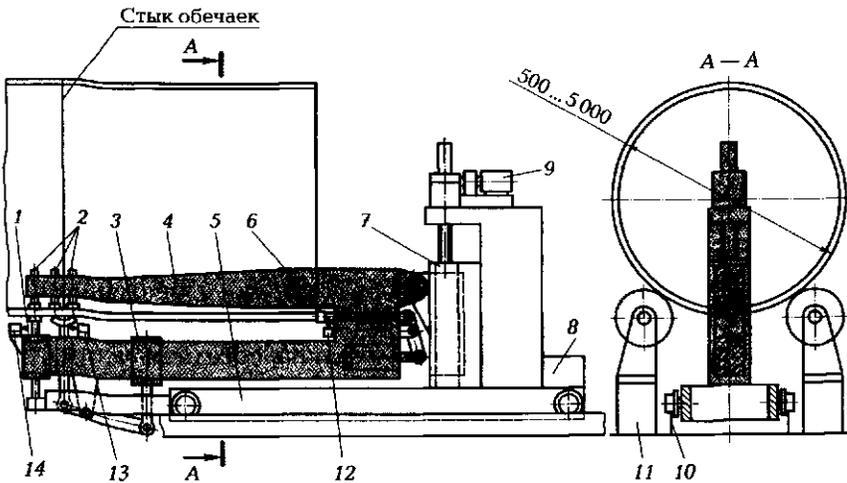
Установка для сборки обечаек по кольцевым стыкам:
